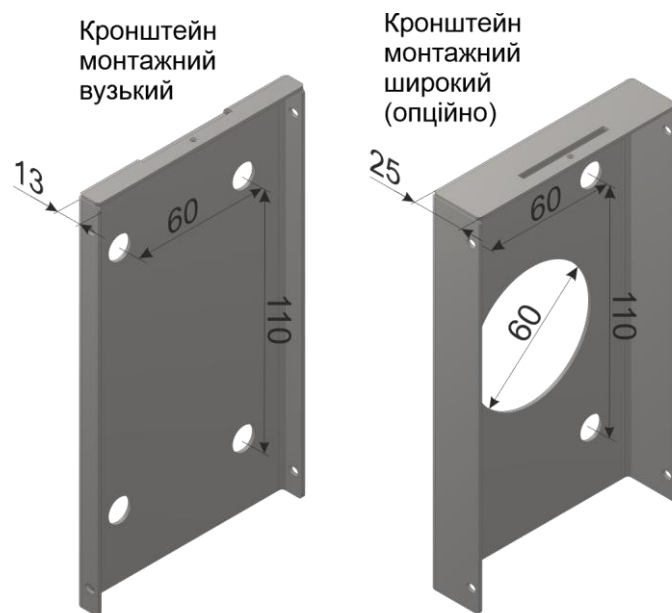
Рекомендації щодо габаритів монтажу на стіну
